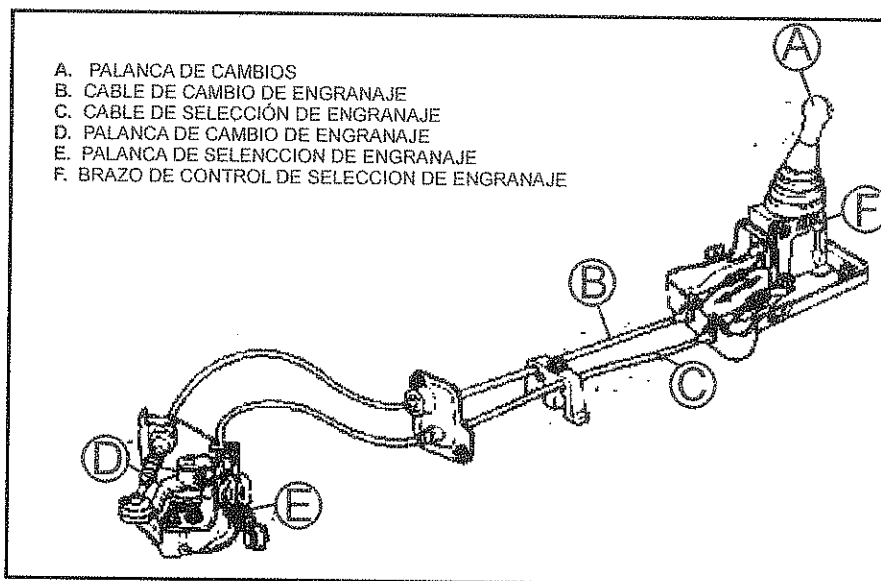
Partes del sistema por cables de cambio de engranajes
